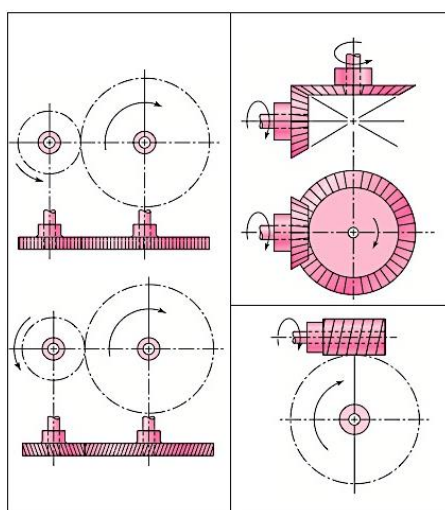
Sistemas de engrenagens associadas em série (a) Engrenagem simples e helicoidal; (b) Engrenagem cônica; (c) Engrenagem com sem fim; retiradas de Budynas e Nisbett (2006)
